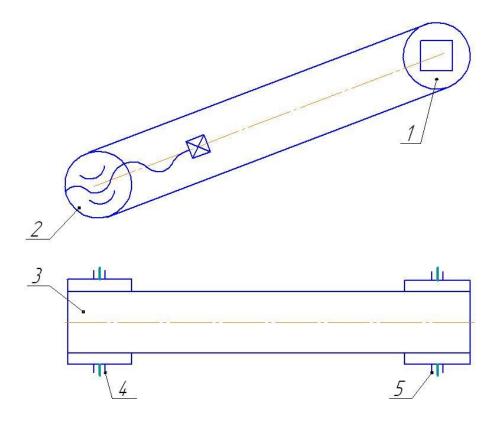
а - Схема установки для зооветобработки овец (Vобразный транспортер).
